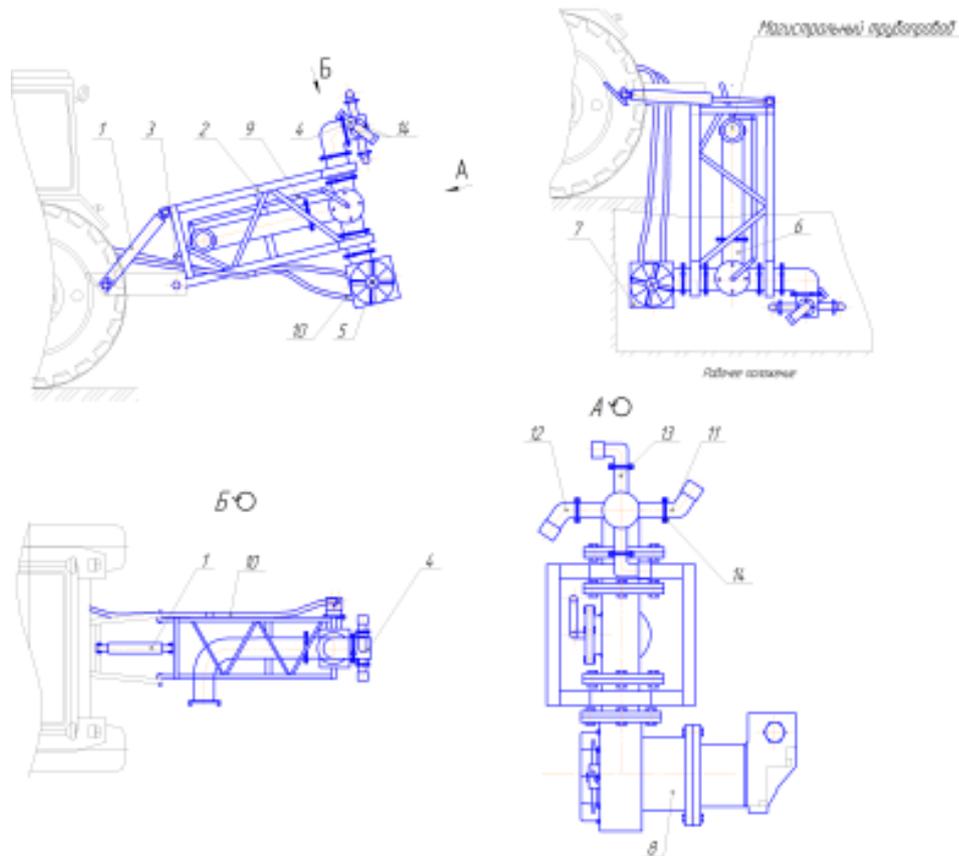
Агрегат для создания однородной массы навоза в лагуне: 1 - гидроцилиндр; 2 - рама кронштейна; 3 - затворное устройство; 4 - блок насадок; 5 - заборное устройство; 6 - измельчающий механизм; 7 - гидромотор; 8 - насос; 9 - затворное устройство; 10 - шланги высокого давления; 11, 12, 13 - насадки, 14 - фланцы
